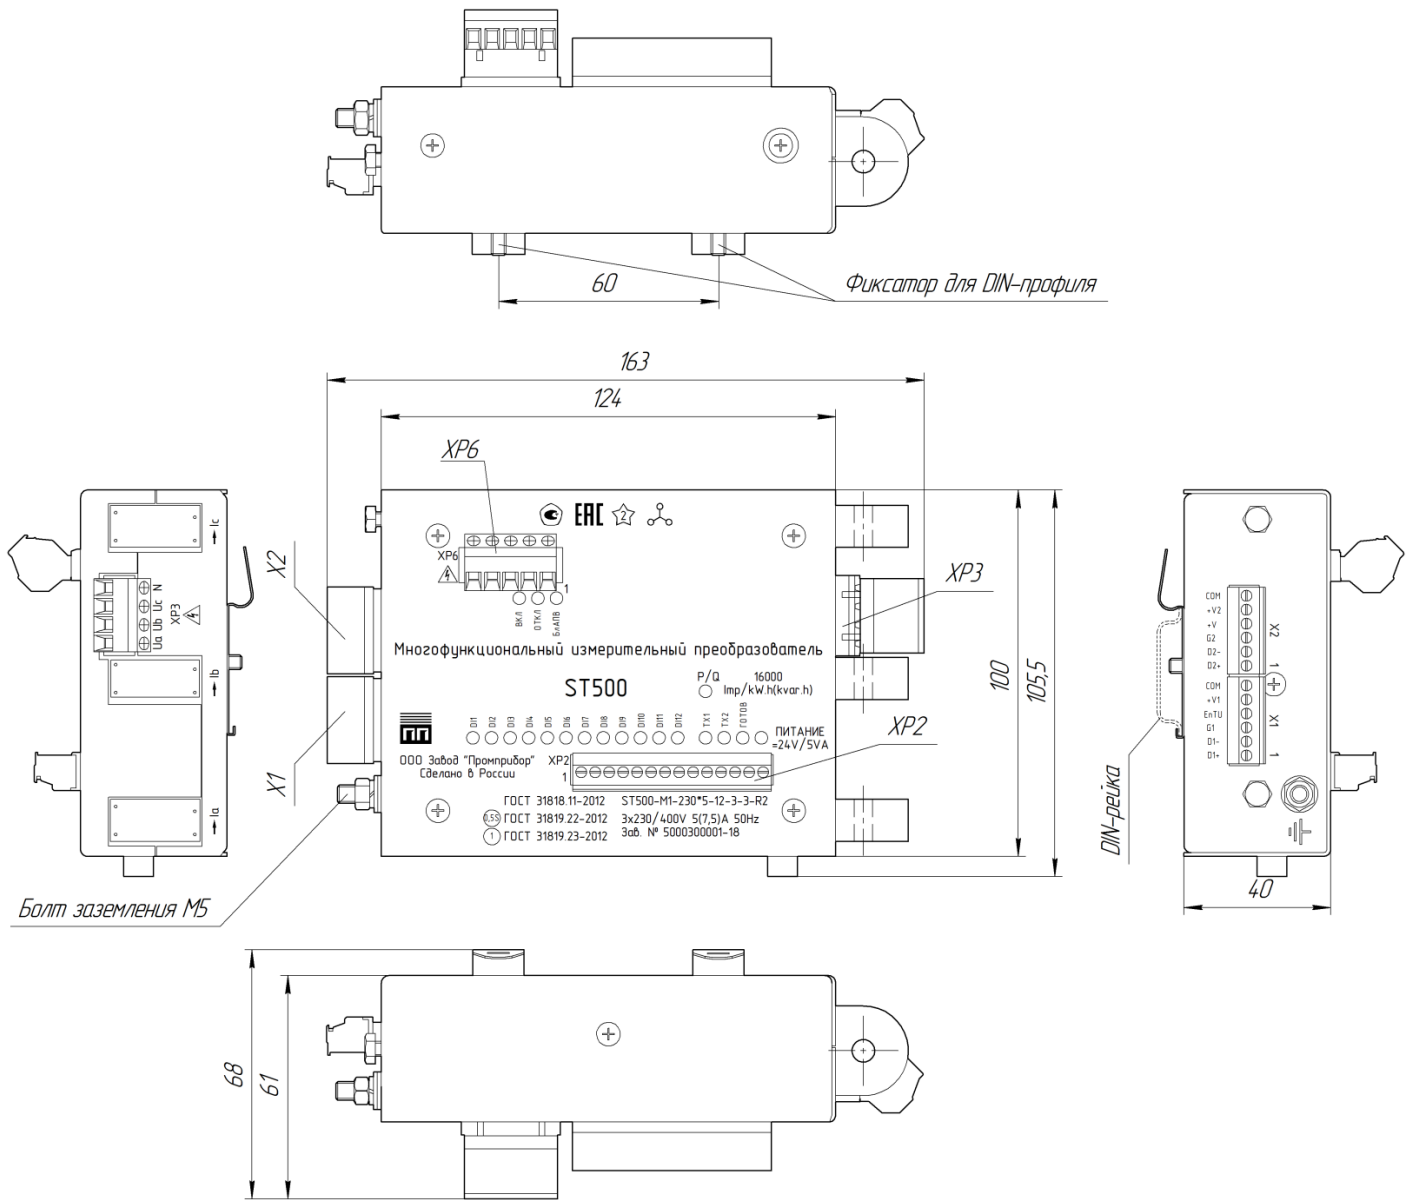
Внешний вид и габаритные размеры МИП
